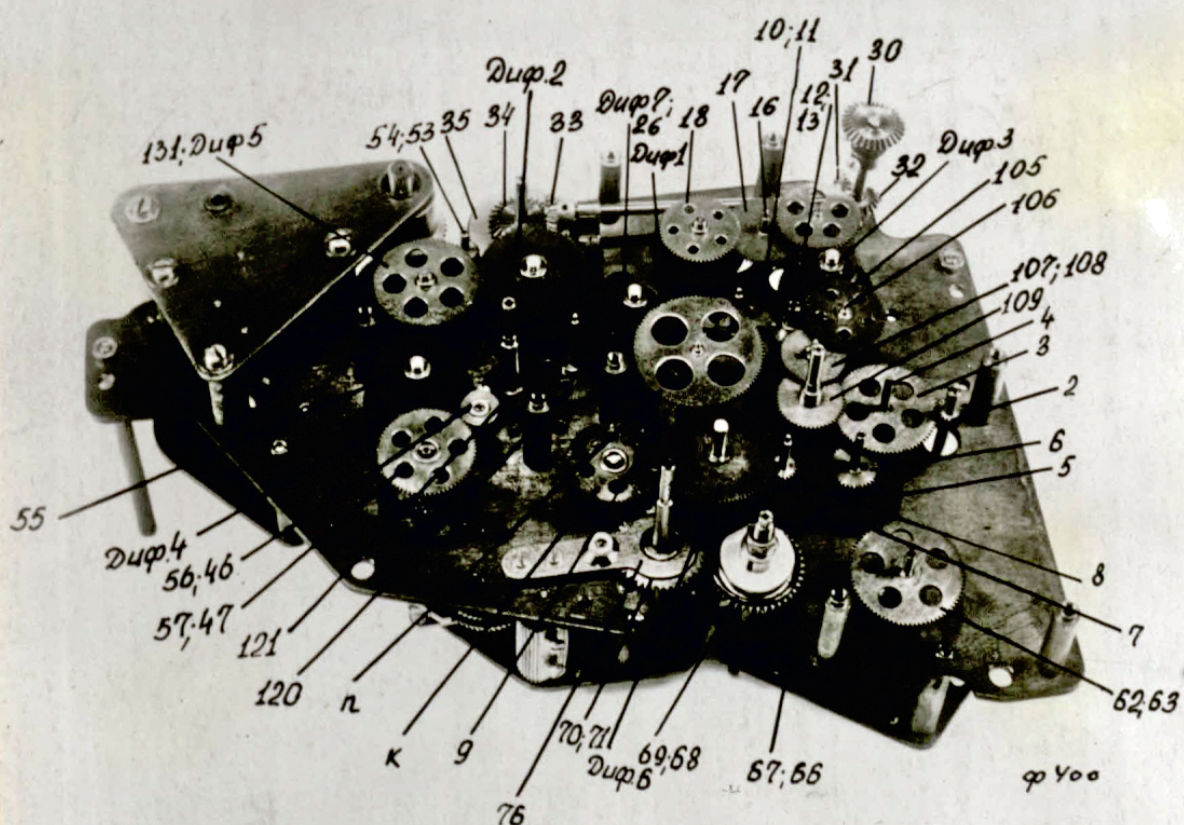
Блок редукторов орбитального и суточного вращения прибора ИМПЧ
